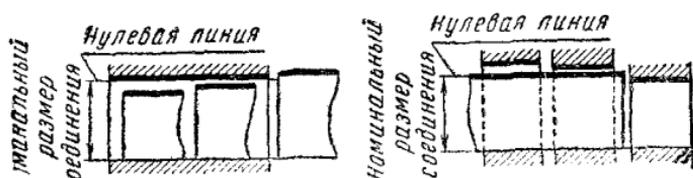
Схема графического построения допусков для отверстия и вала
